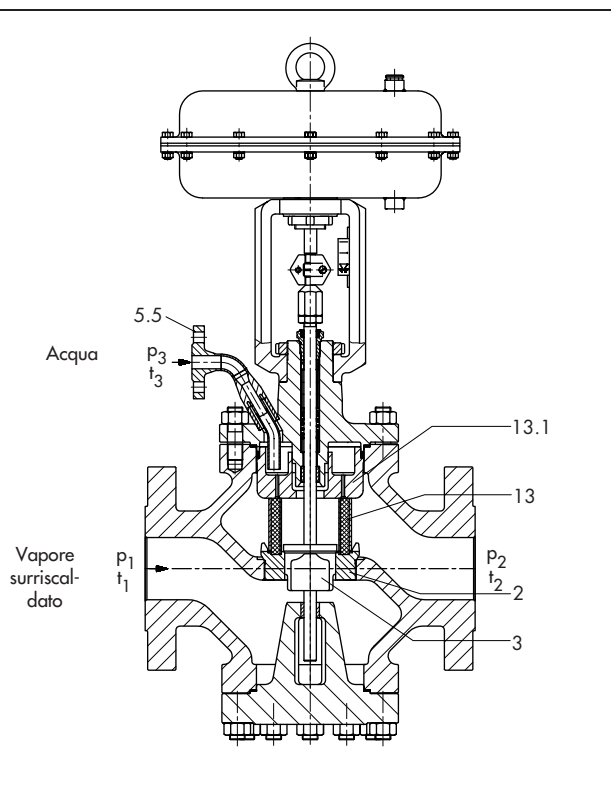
· Desurriscaldatore pneumatico Tipo 3284-1 con attacchi flangiati, otturatore standard e attuatore Tipo 3271
